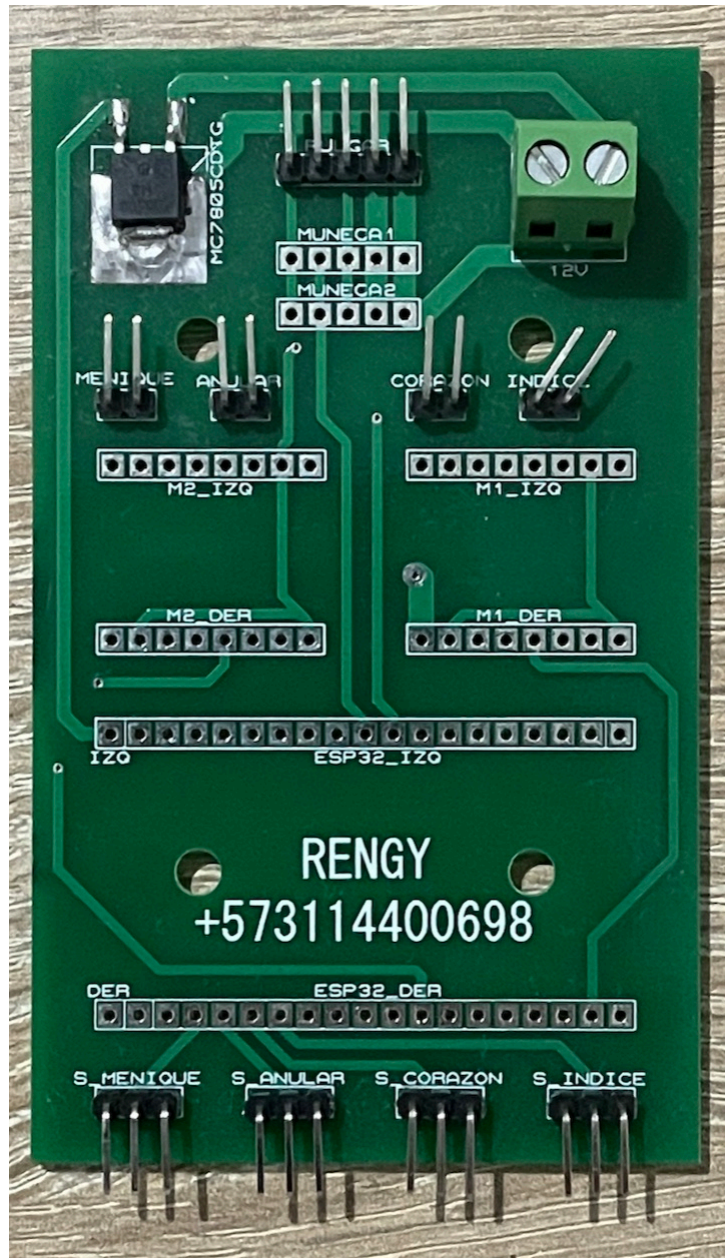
Primer diseño de PCB (ESP-WROOM32 WiFi™-Bluetooth™).
